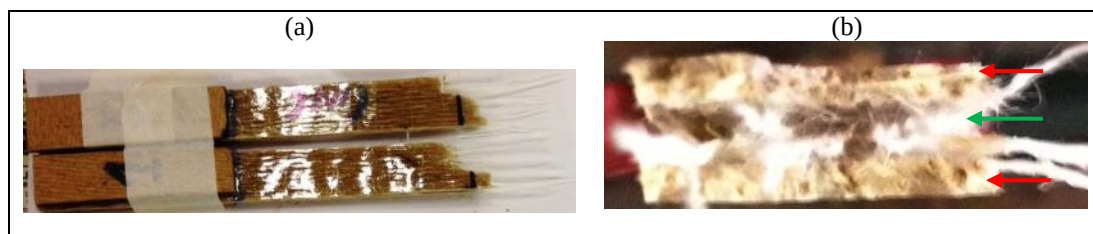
Aspecto da fratura do laminado Juta/Vidro/Juta (a) Corpo de prova ensaiado (b) Superfície de fratura.
